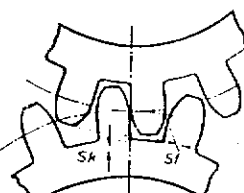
Par de ruedas dentadas engranando entre sí. S_f) juego de los flancos (exagerado en el dibujo); S_k) juego de la cabeza.
